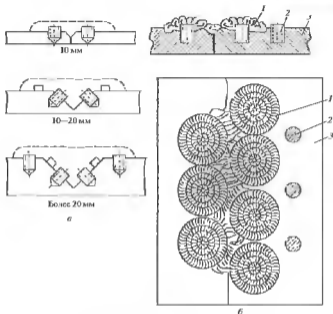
Сварка чугуна с применением упрочняющих шпилек:
